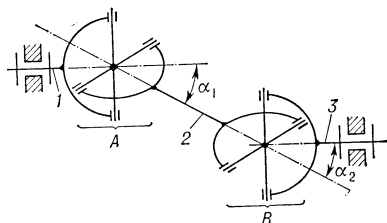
Схема двойного шарнира Гука: 1 — ведущий вал; 2 — промежуточный вал; 3 — ведомый вал; *A, B* — универсальные шарниры.
